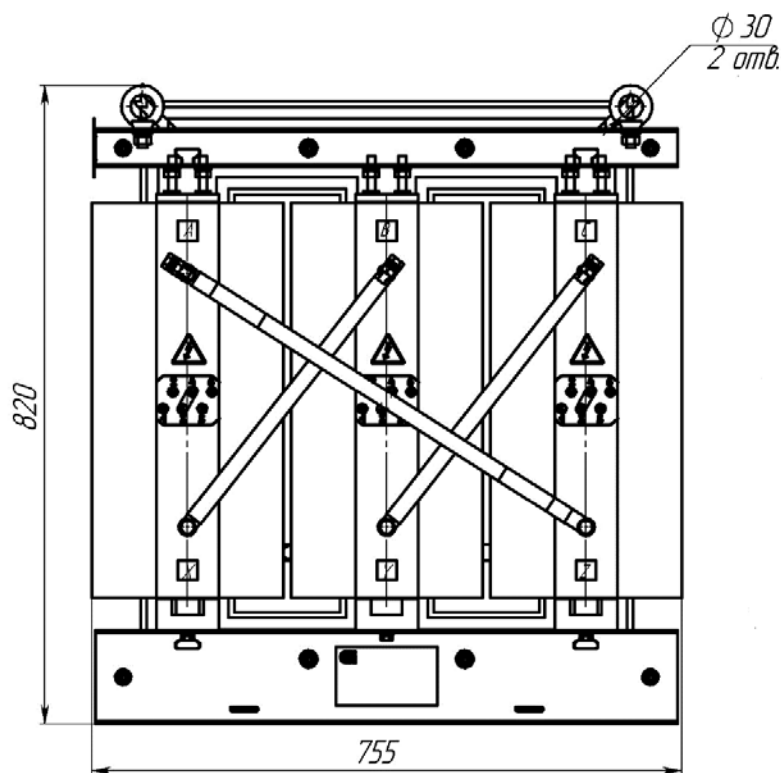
Габаритный эскиз ТЛС-63 (А)
